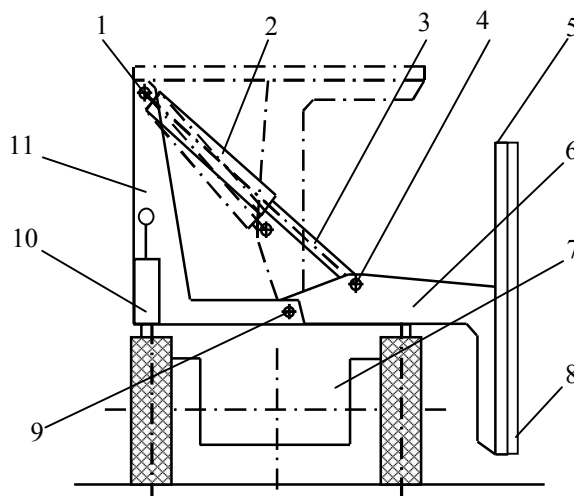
Пристрій розгортання силового бар'єра з транспортного положення у робоче
